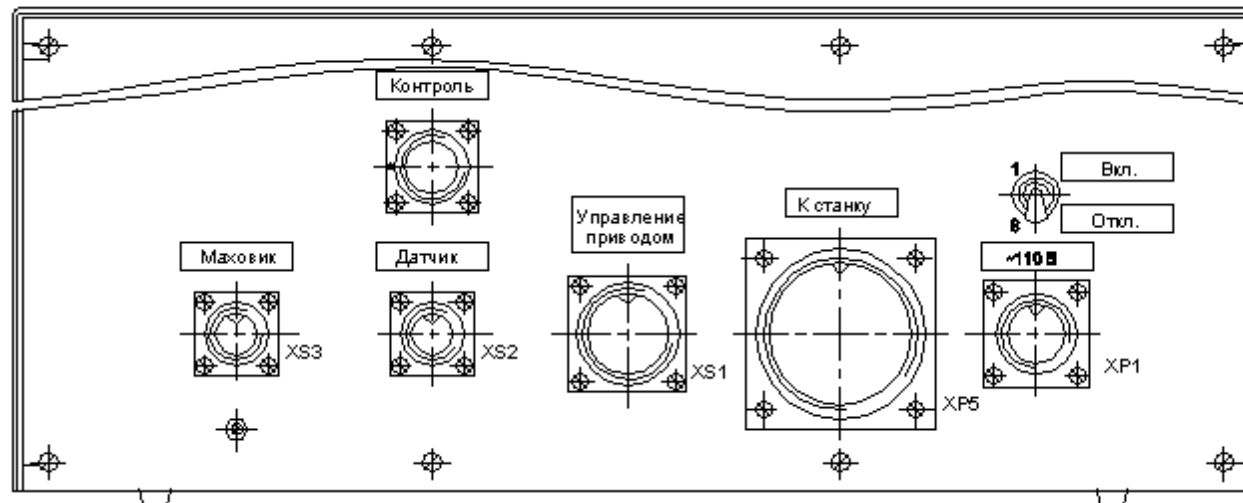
Внешний вид и габаритные размеры K530-01
